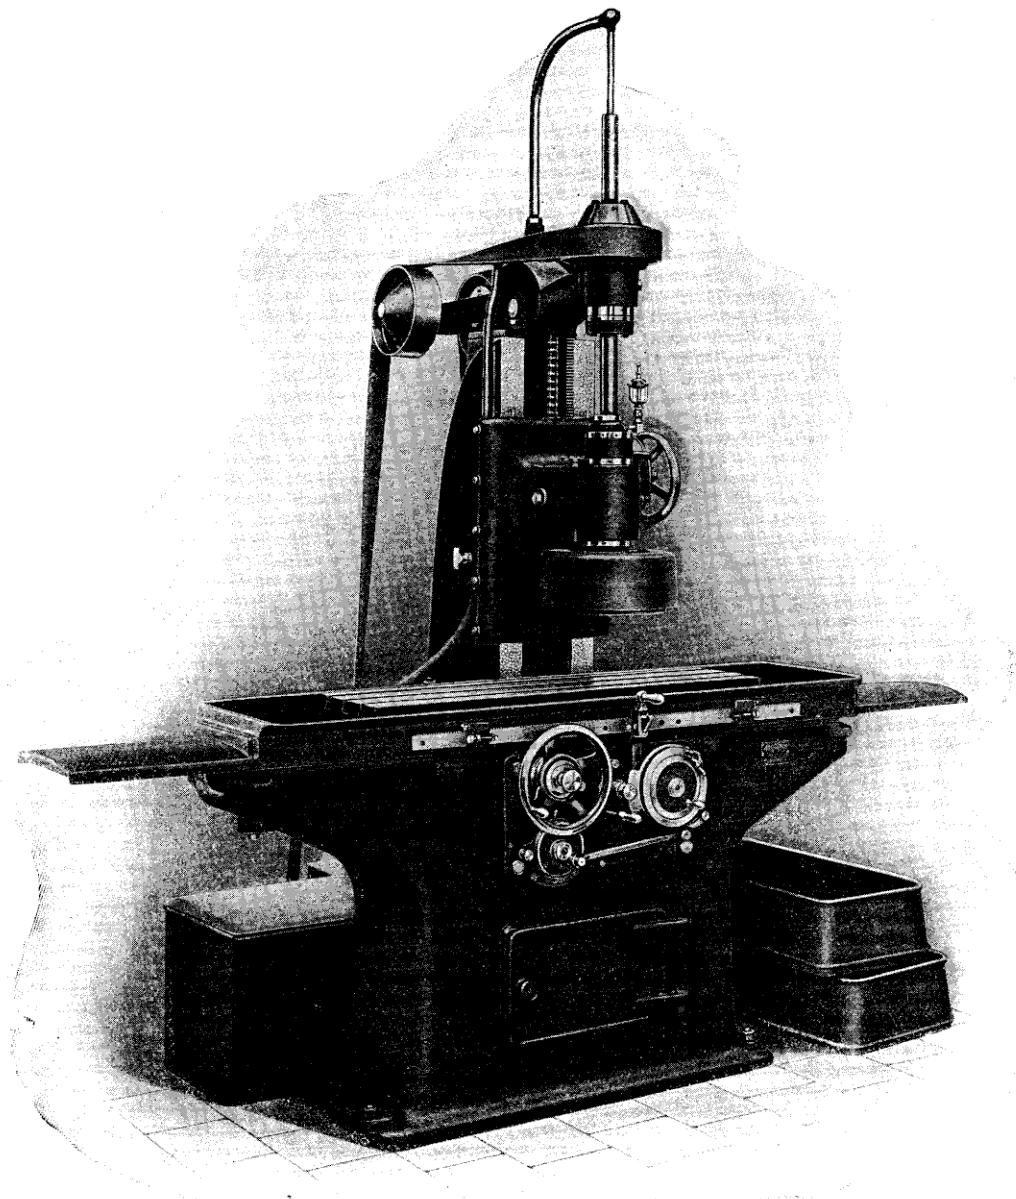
Machine de précision à rectifier les surfaces planes.
